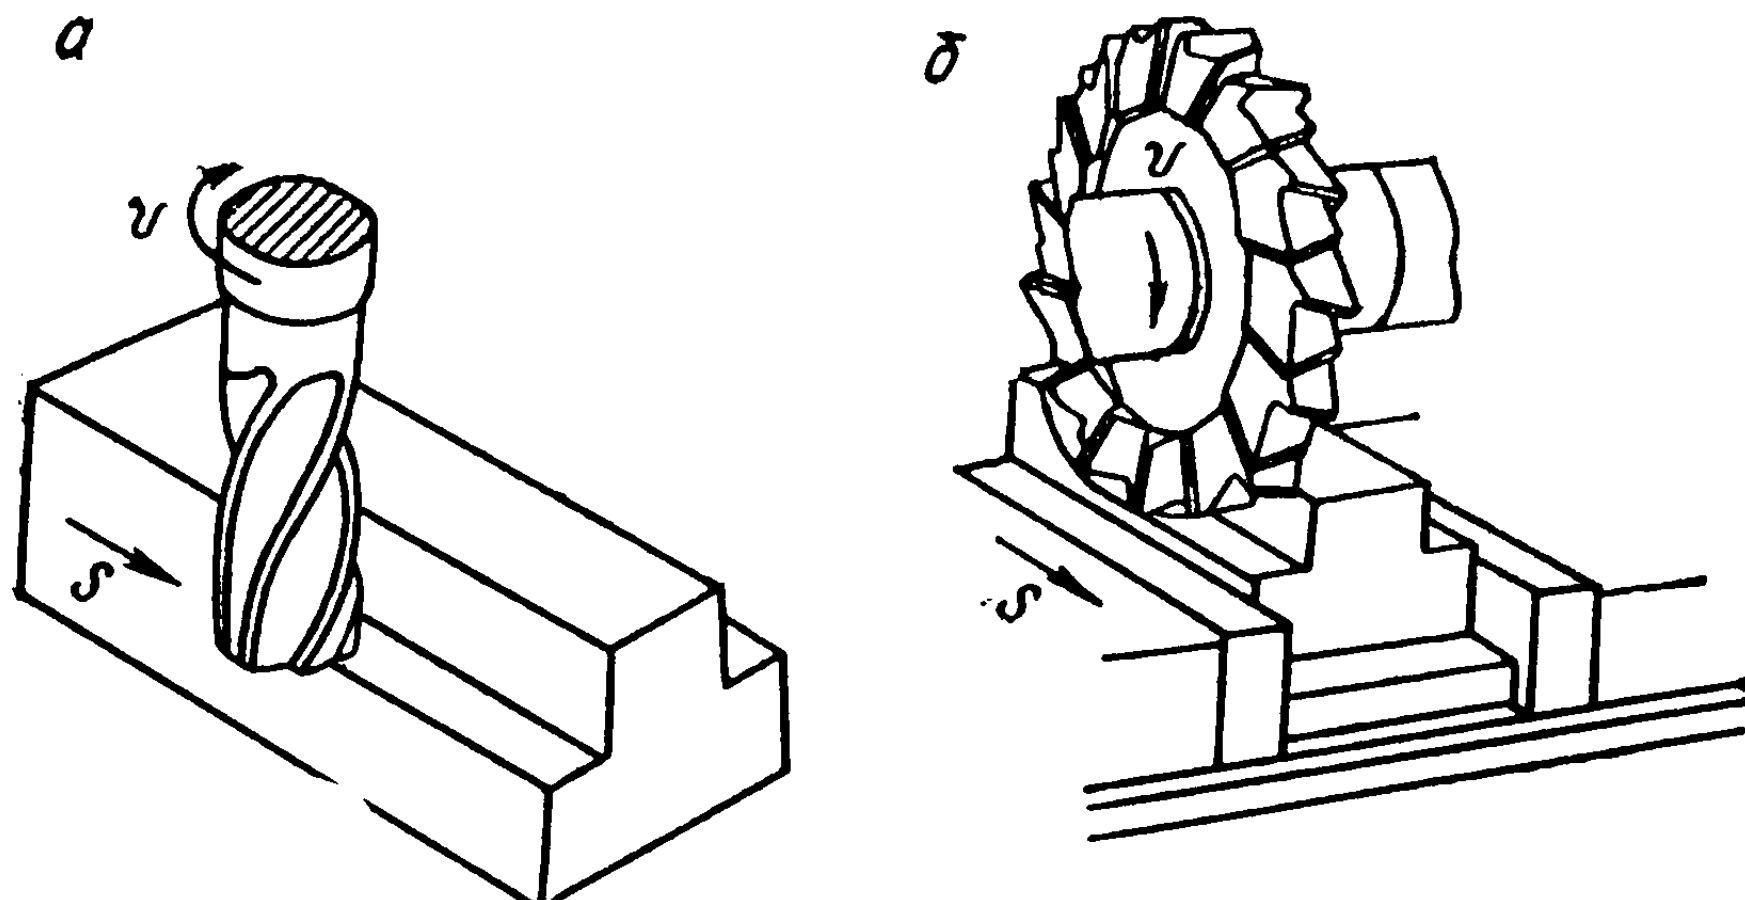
Фрезерование двух уступов концевой и дисковой фрезой.
